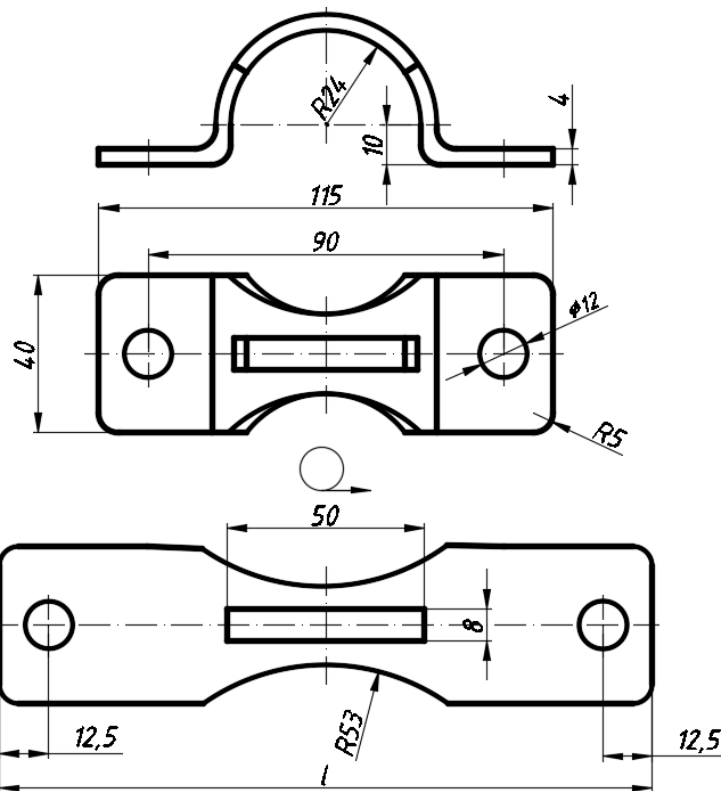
Образец выполнения чертежа детали, изготавливаемой гибкой.
